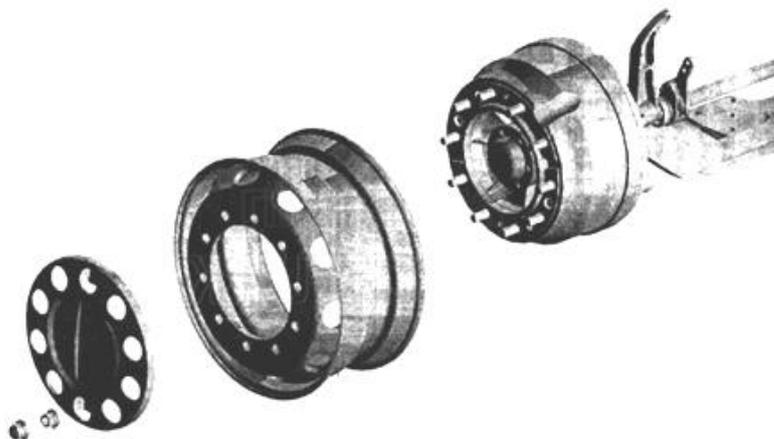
Схема установки колес автобуса ЛИА3-5256
